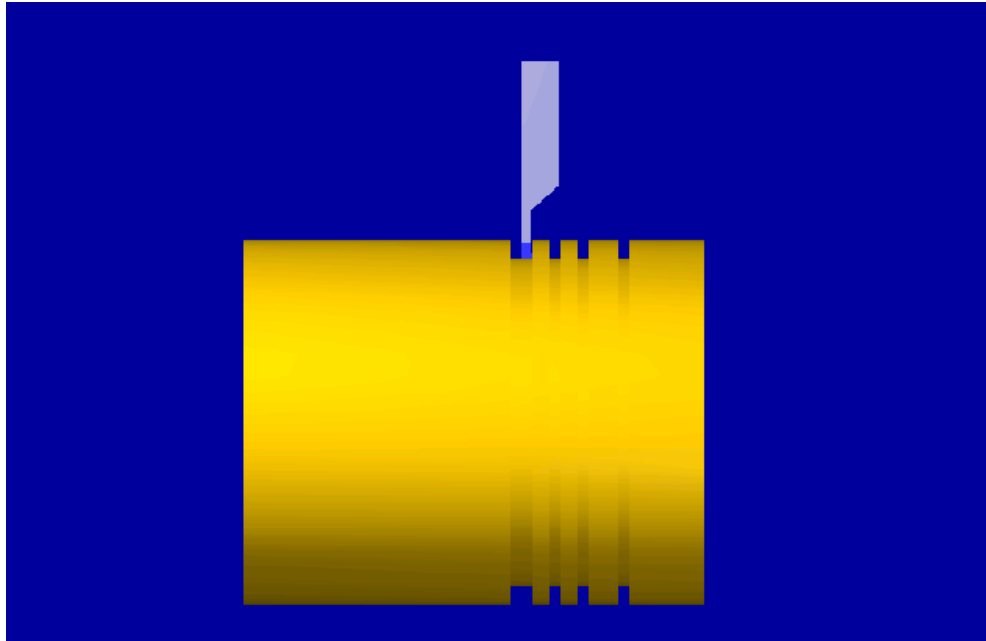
Візуалізація обробки деталі «Поршень Д-112-94-1438»
